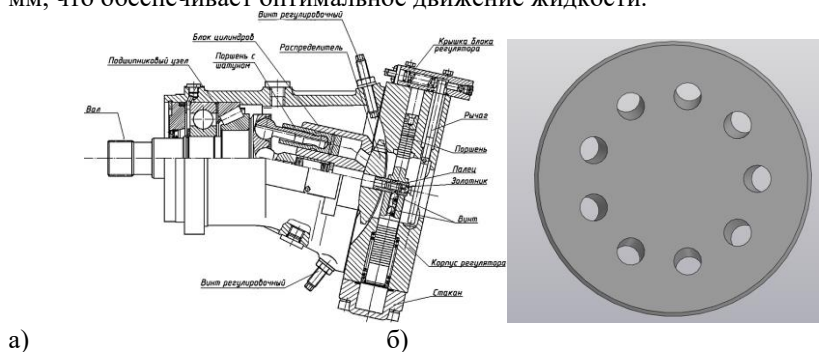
Аксиально-поршневой регулируемый насос типа 313: а) устройство; б) 3D-модель блока цилиндров с питающими окнами
